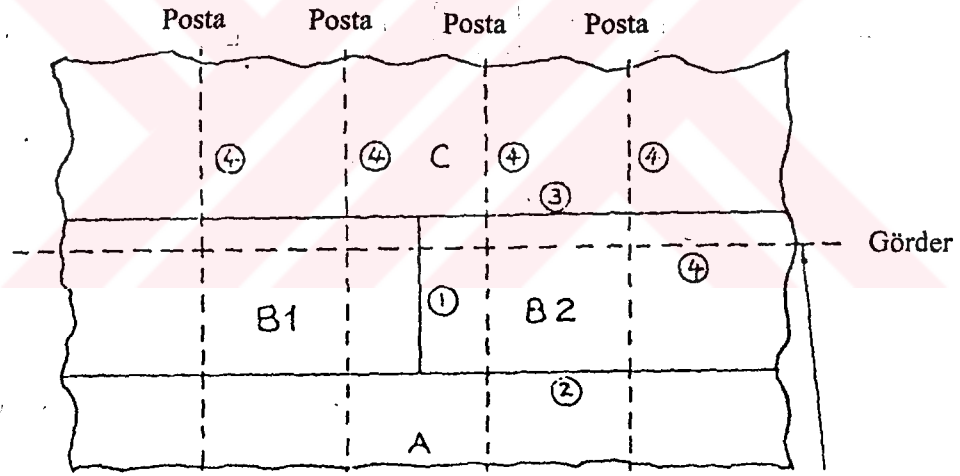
Bir T kesişmesindeki kaynak detayı
